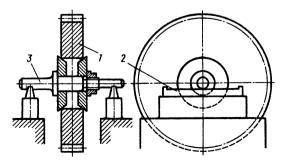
Схема балансировки колеса на призмах: I — зубчатое колесо; 2 — призма; 3 — оправка
